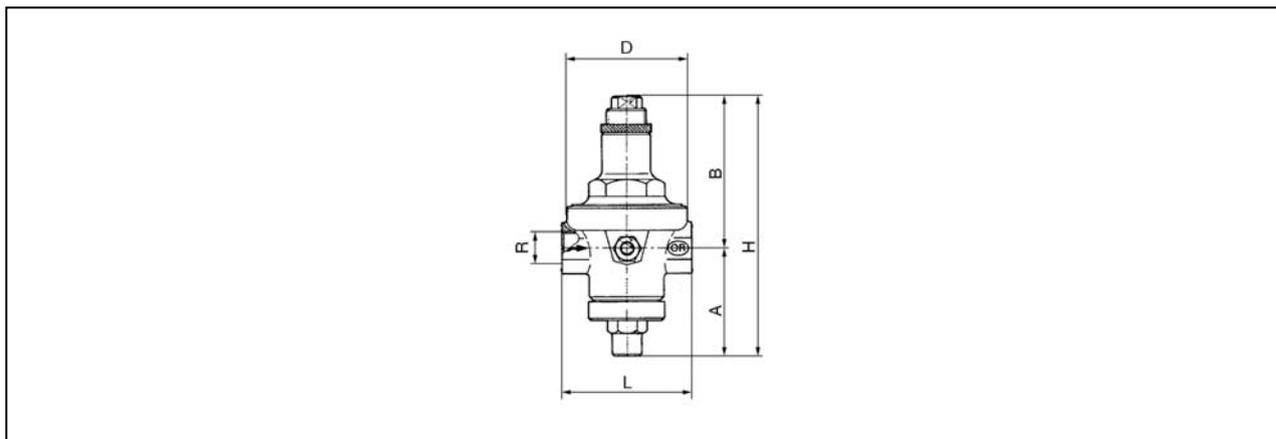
Габаритные и присоединительные размеры клапана типа RP204.
